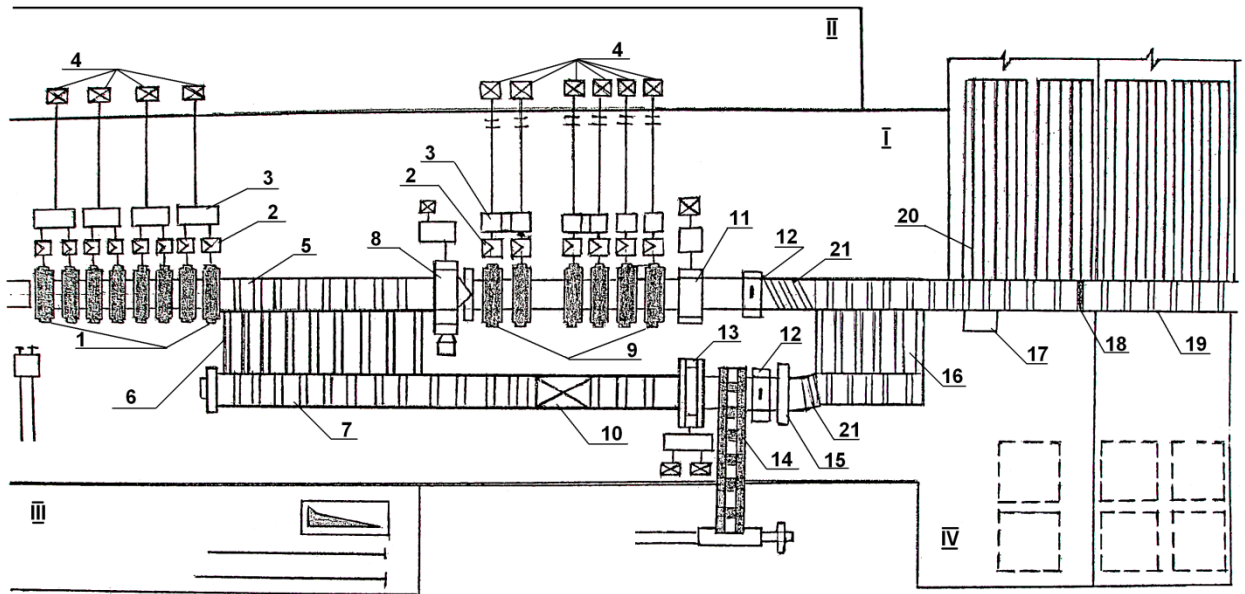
Схема розташування обладнання безперервно-заготівельного стану 730/500:
